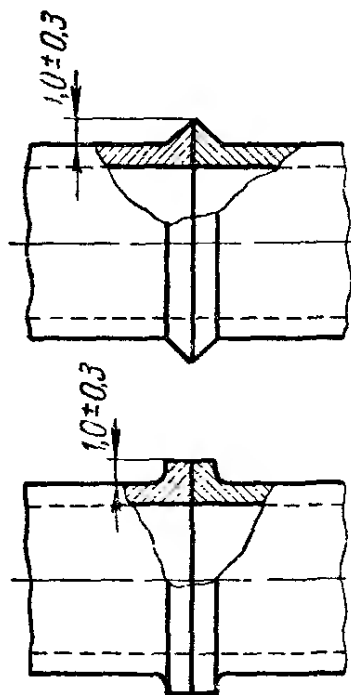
Способы подготовки кромок тонкостенных труб из стали 1Х18Н9Т для аргоно-дуговой сварки вольфрамовым электродом
